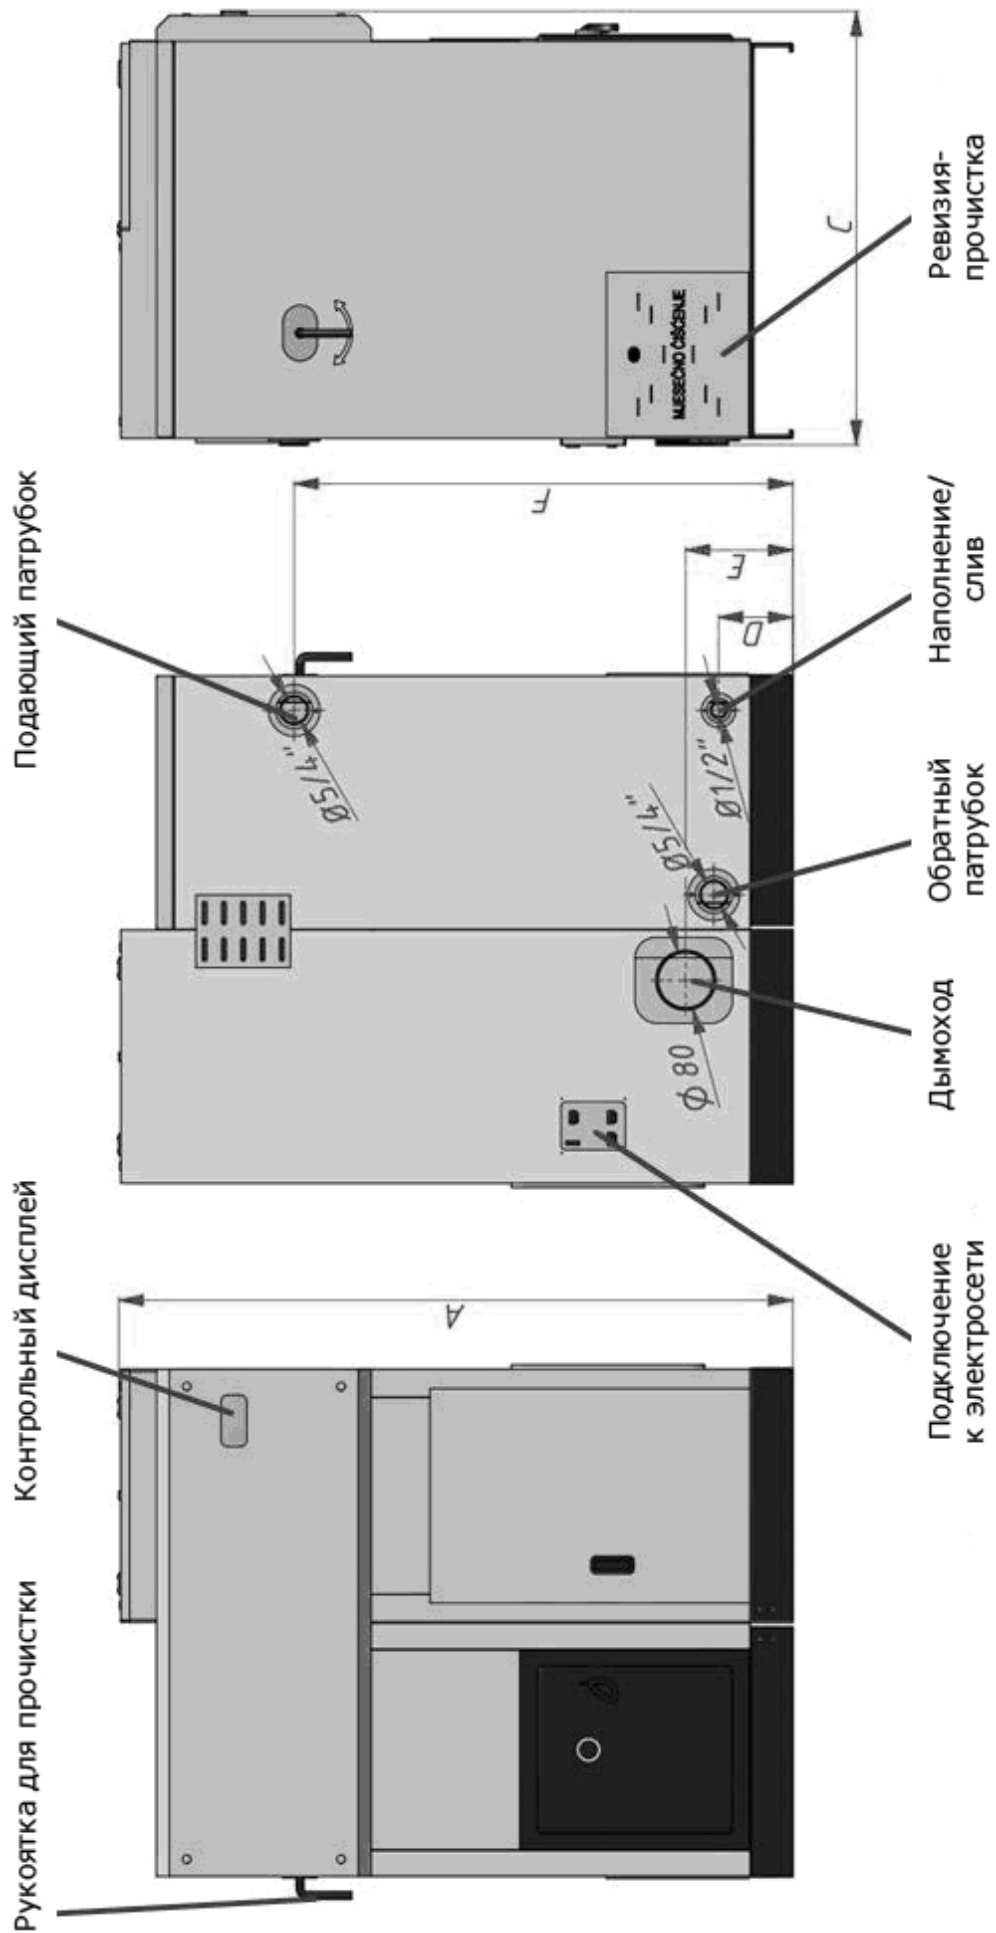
Вид и размеры котла WIRBEL™ ECO SMT 35÷100 кВт
